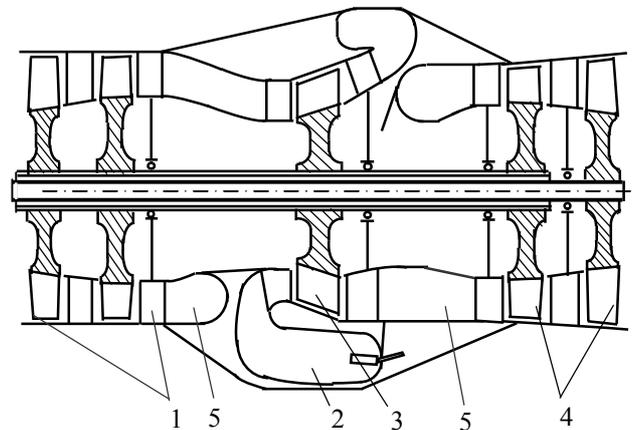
Схема газотурбинного двигателя с ТКО: 1 – компрессор; 2 – камера сгорания; 3 – ТКО; 4 – силовая турбина; 5 – переходный канал
